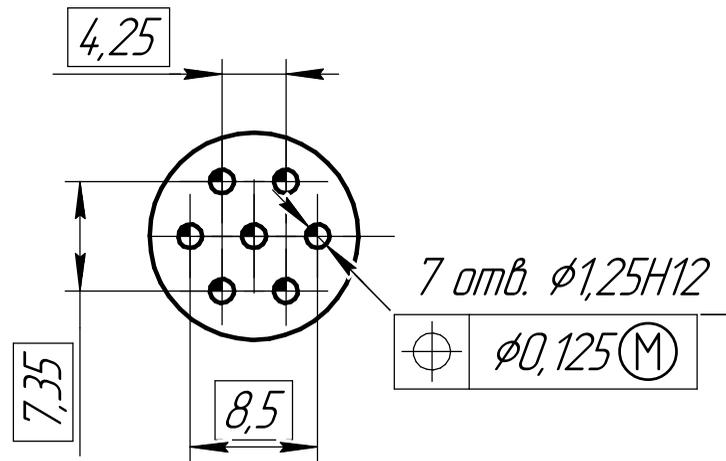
Разметка отверстий для ОСН-25-7/18...П-...
